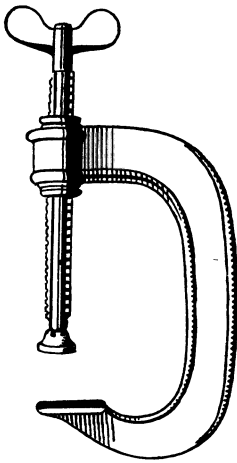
Bügelschraubzwinde mit Schnellpannung.
